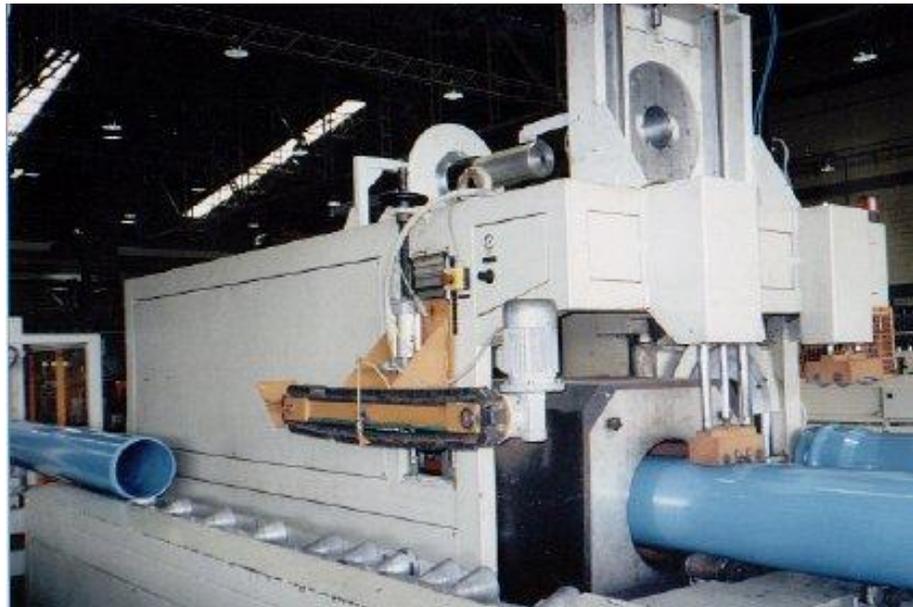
Máquina Campaneadora IPM 500
